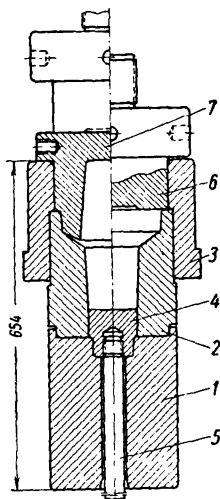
Общий вид штампа для первой операции штамповки ступицы: 1 — нижняя часть матрицы; 2 — матрица; 3 — направляющее кольцо; 4 — дно; 5 — выталкиватель; 6 — пуансон второй высадки; 7 — пуансон первой высадки
